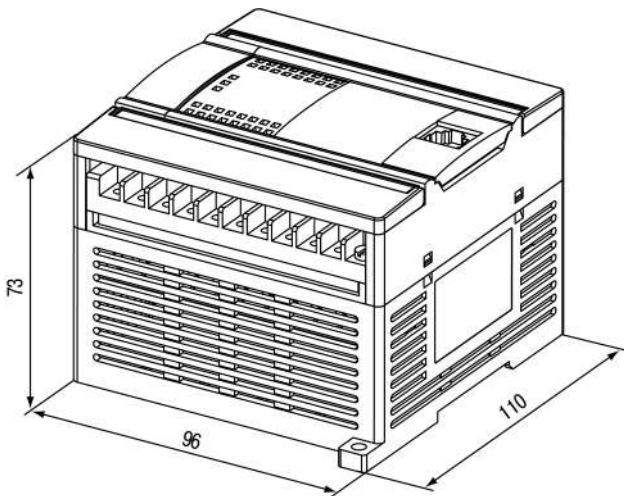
Габаритний кресленик ПР110-х.12х.8х
